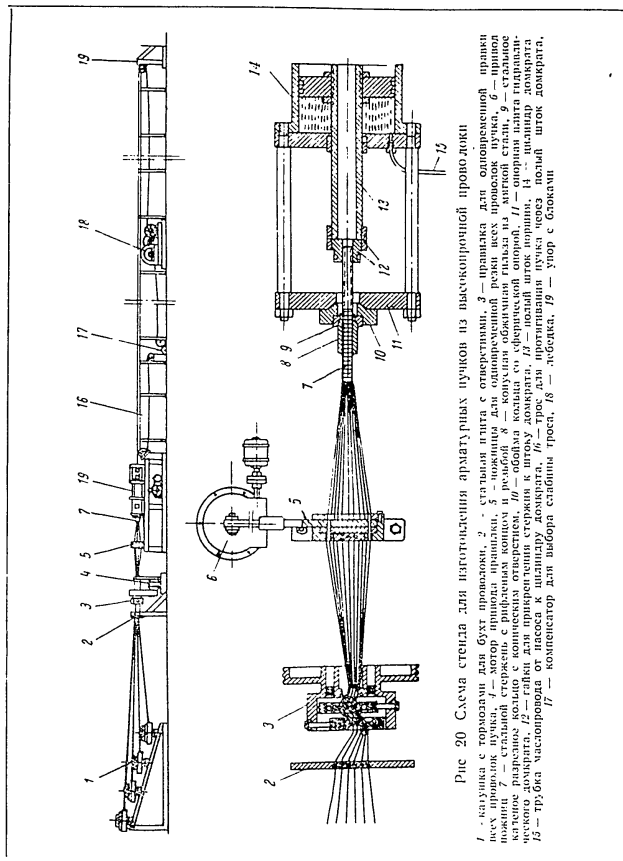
Схема станка для изготовления арматурных пучков из высокопрочной проволоки
